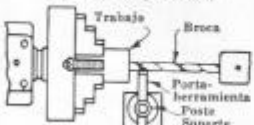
Uso de un portaherramientas para estabilizar la punta de la broca
